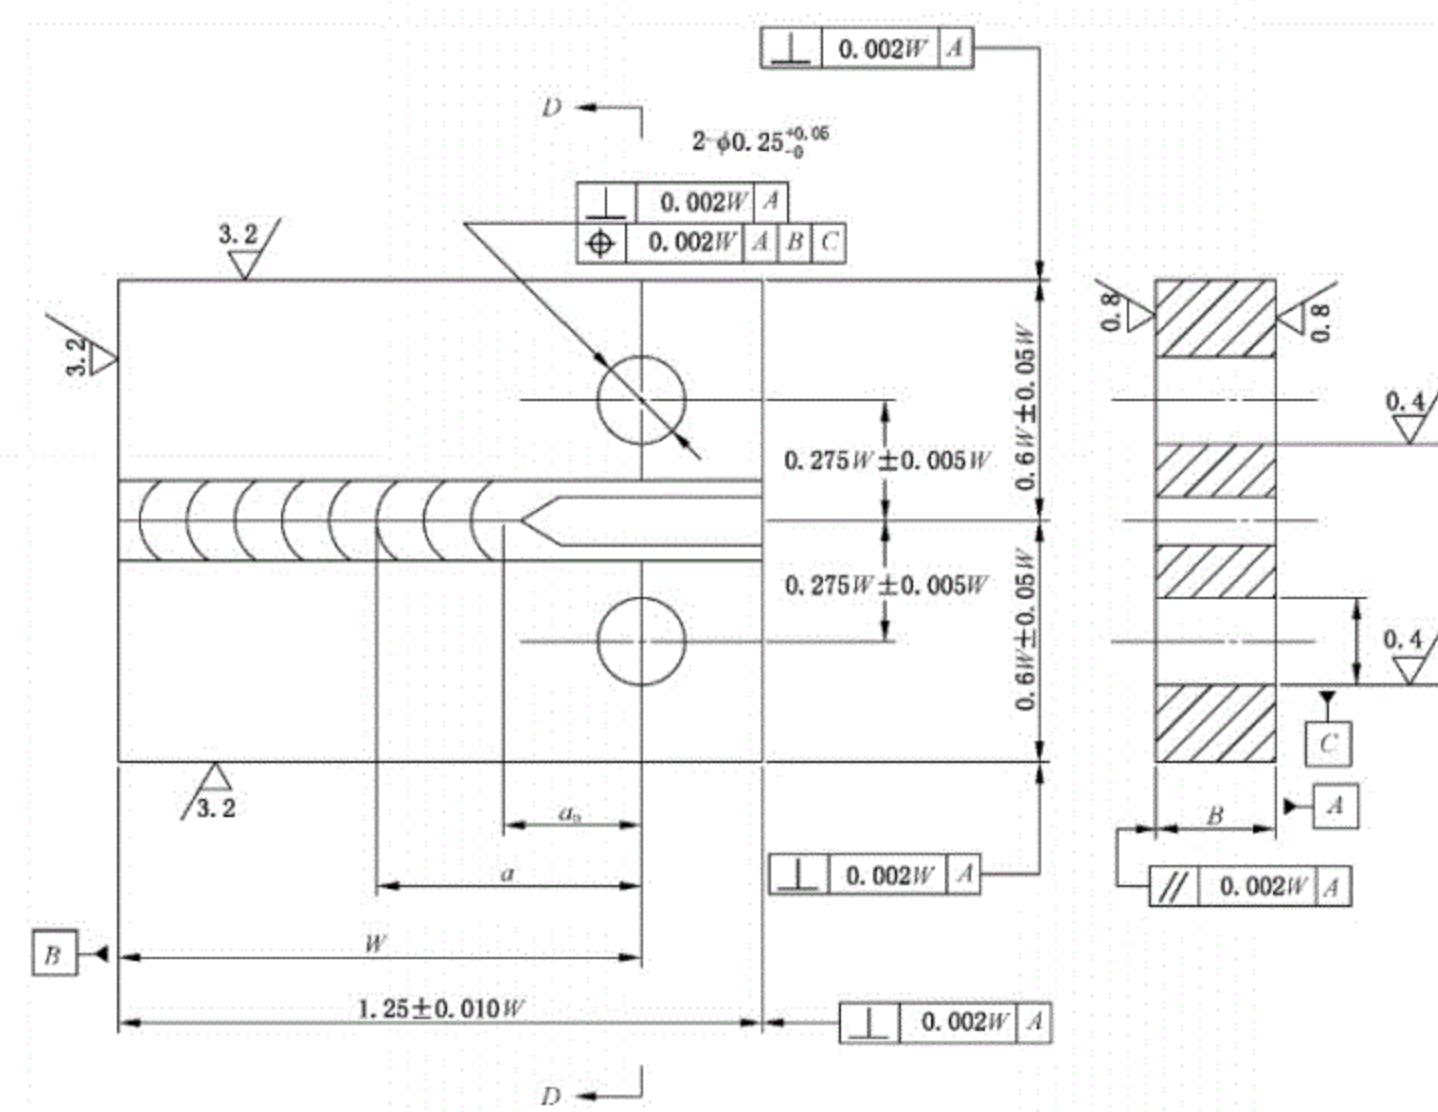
焊接接头疲劳裂纹扩展速率试样(CT 样)
